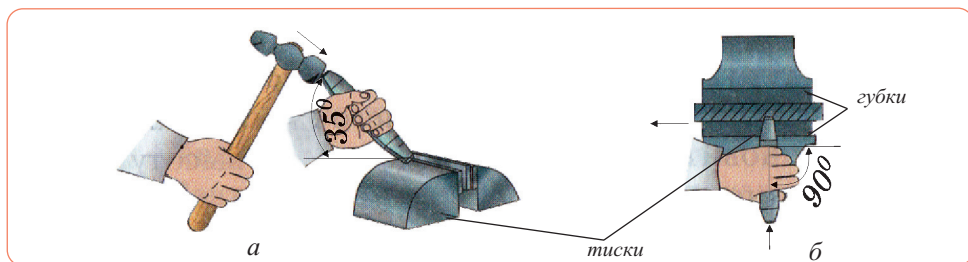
Положение зубила в тисках: а – при рубке припуска; б – при рубке металла на части
